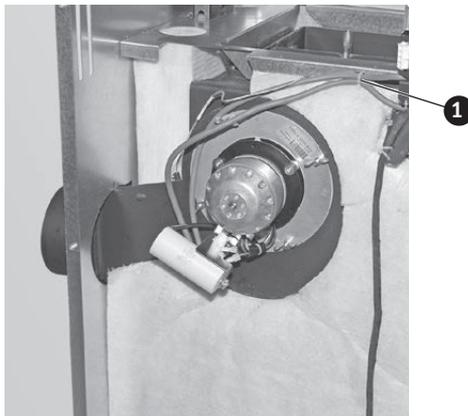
Riavvitare il ventilatore gas combusti ruotato di 90°
